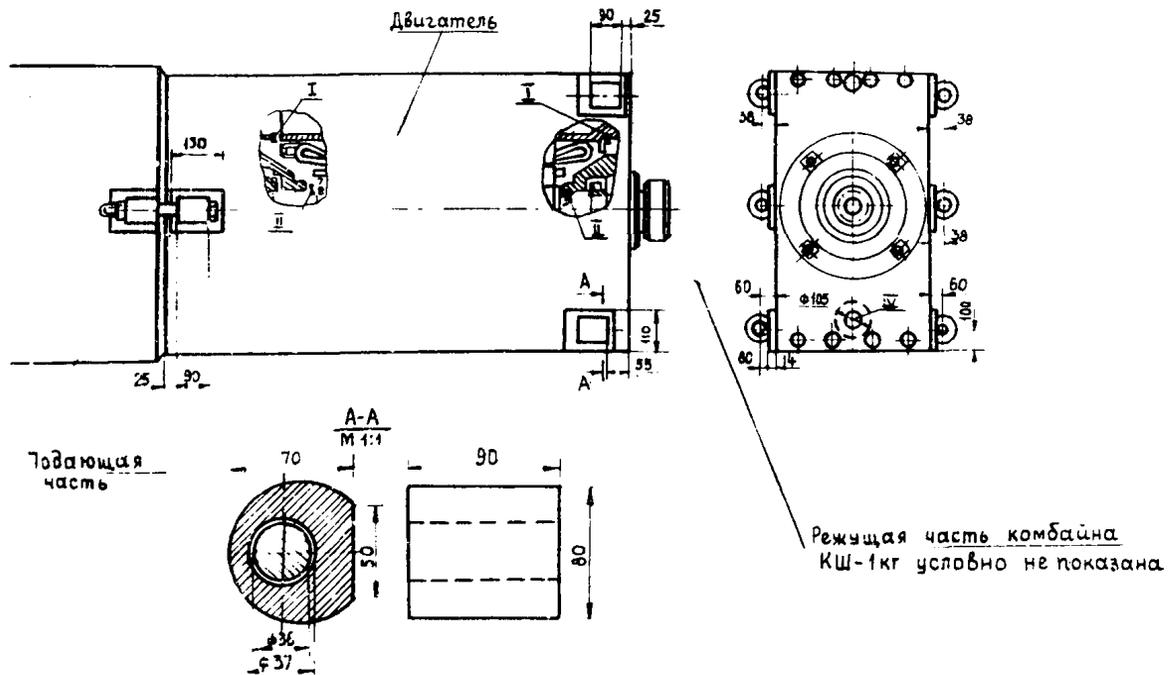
Усиление соединения электродвигателя с подающей и режущей частями комбайна КШ-1кг с помощью дополнительного болтового соединения
